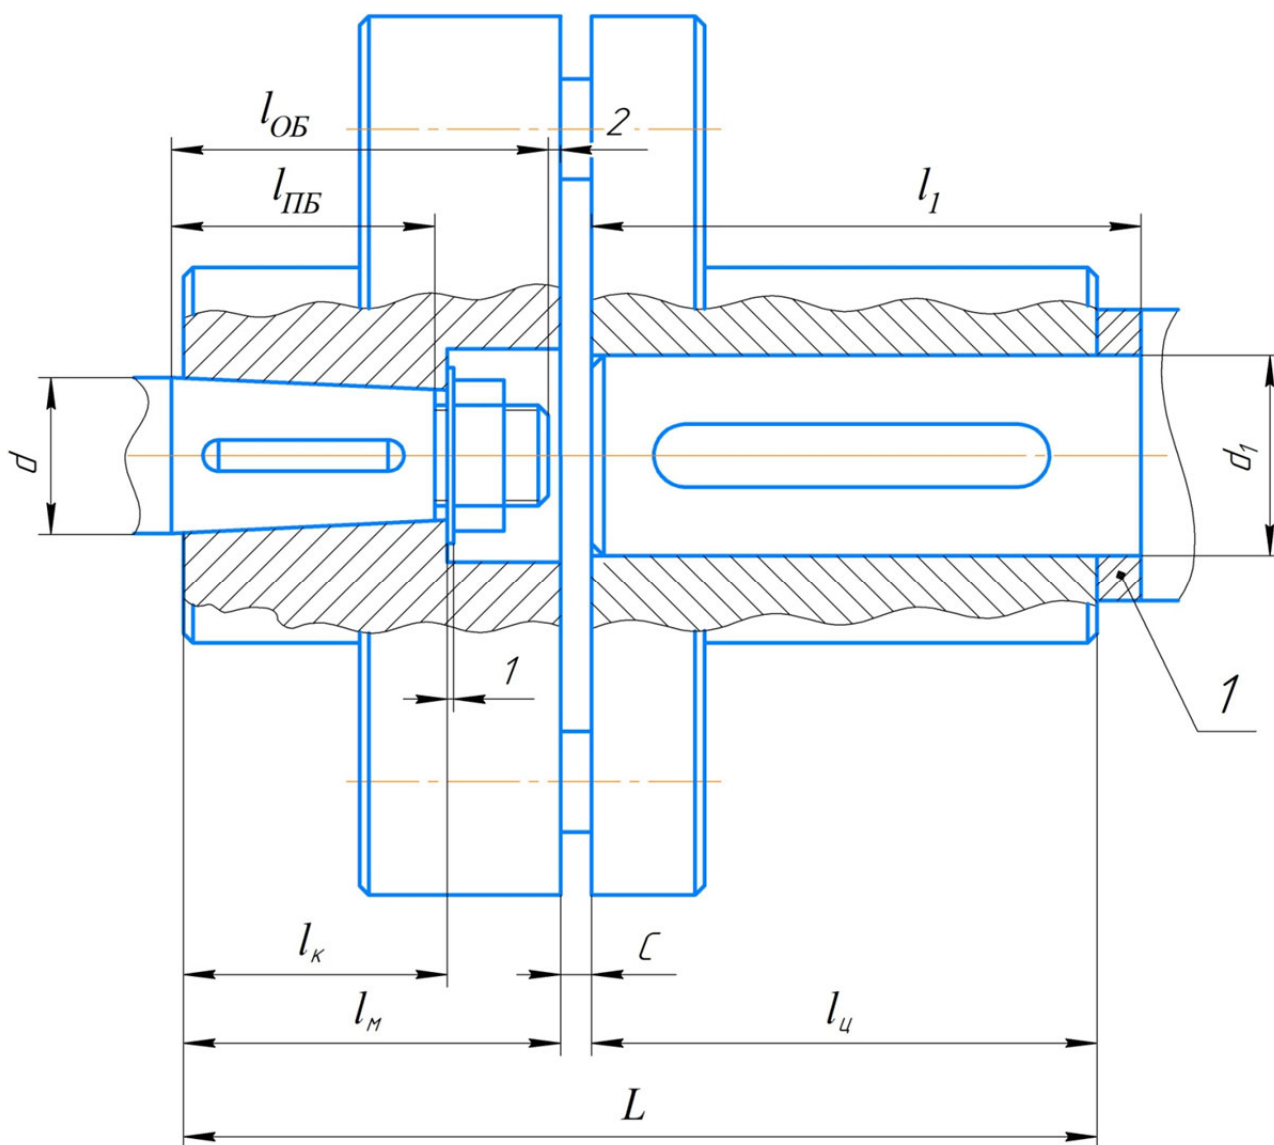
Установка упругой втулочно-пальцевой муфты на валах привода:
